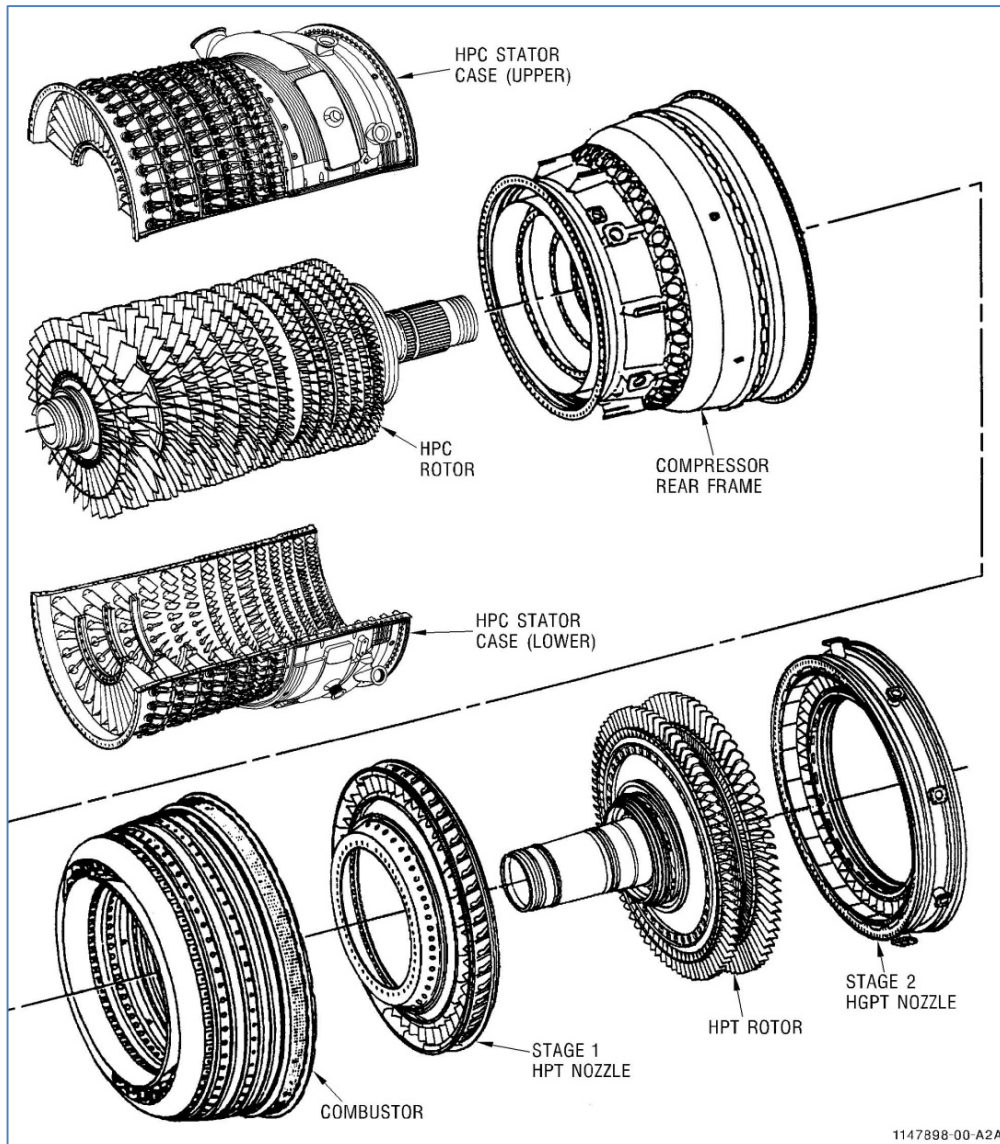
B. COMPONENTES PRINCIPALES DE UNA TURBINA A GAS
